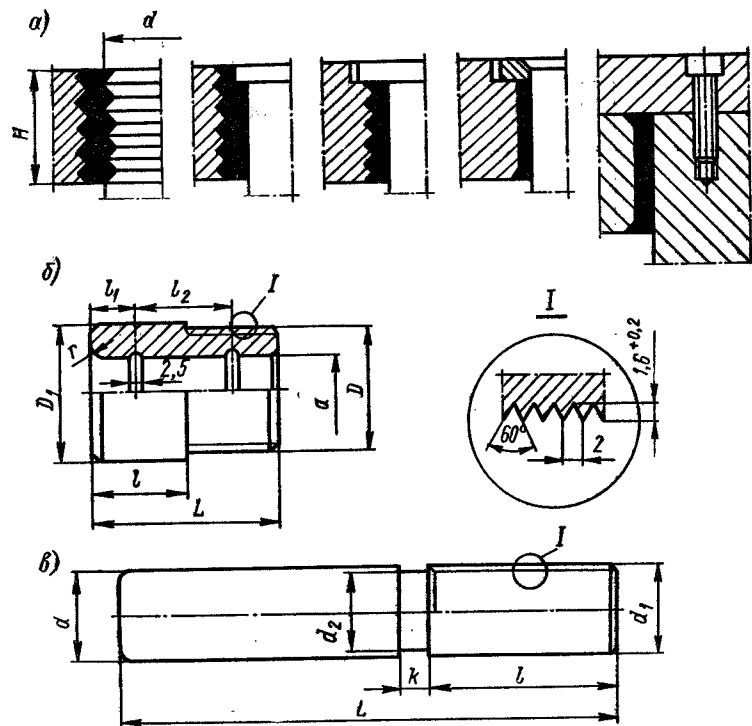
Соединение деталей штампов быстротвердеющими пластмассами: а — способы подготовки поверхности под заливку; б — нормализованная направляющая втулка; в — нормализованная направляющая колонка
